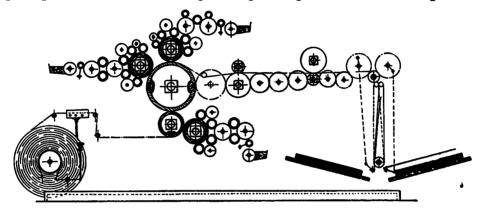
Zweifarben-Rotationsmaschine für Werk- und Illustrationsdruck der Maschinenfabrik Augsburg
